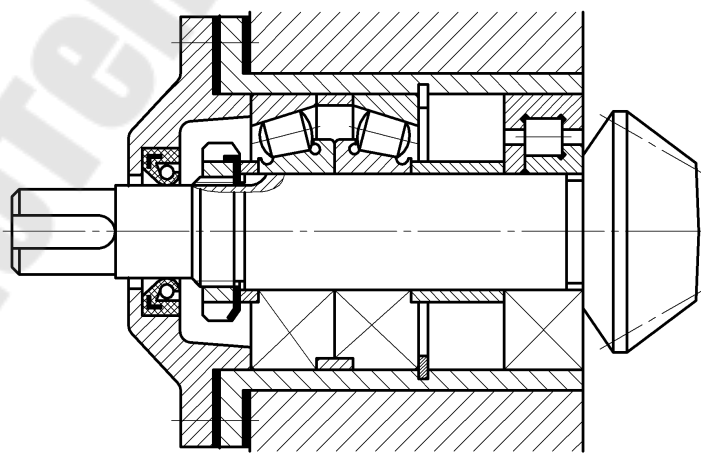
Подшипниковый узел на роликоподшипниках: левая опора – фиксирующая, правая – «плавающая»
